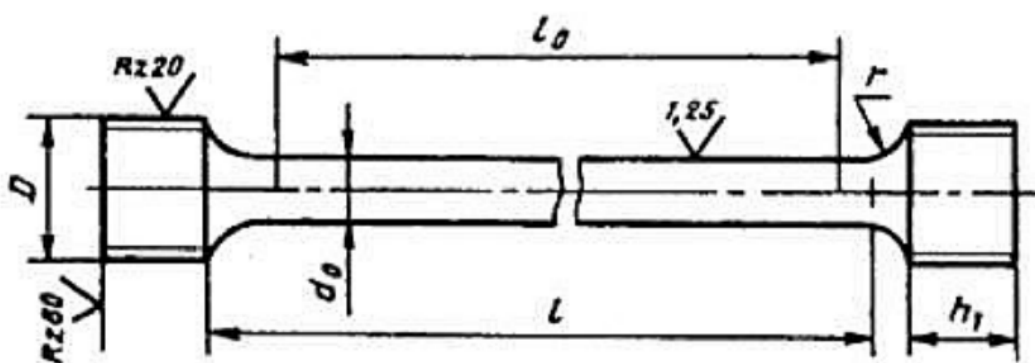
Чертёж цилиндрических образцов согласно ГОСТ 1497-84
